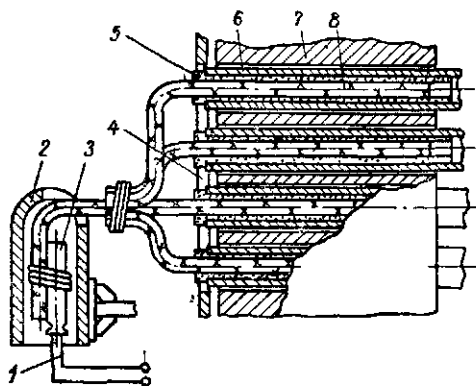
Расположение шнуровых зарядов при закреплении трубок энергией взрыва. 1 — магистральный провод; 2 — защитный кожух; 3 — электродостанов; 4 — защитный лист; 5 — центрирующая втулка; 6 — трубка; 7 — трубная доска; 8 — заряд ВВ.
